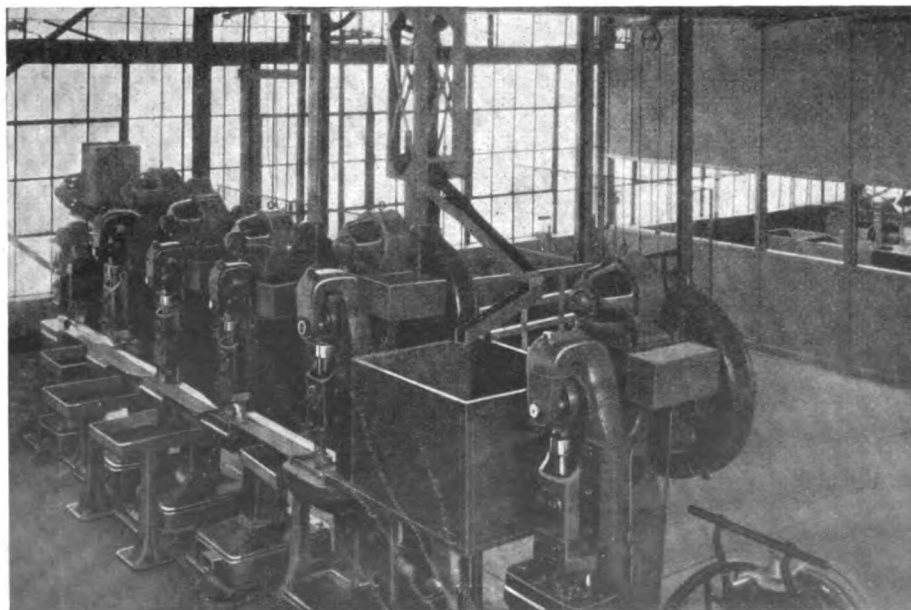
Schwerkraftförderer von Maschine zu Maschine.
